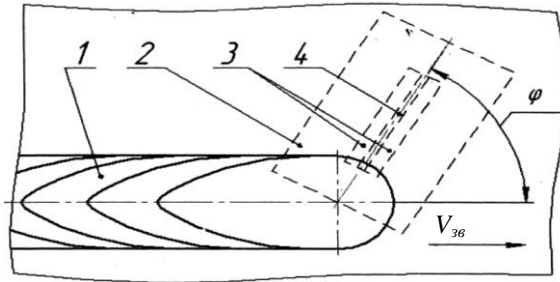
Схема розташування магнітної головки: 1 – зварювальна ванна; 2 – магнітна головка; 3 – загнітопровід головки; 4 – робочий зазор головки
